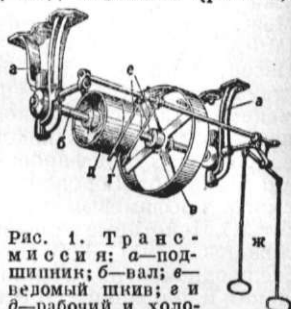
Трансмиссия: а — подшипник; б — вал; в — веревный шкив; г и д — рабочий и холостой шкивы; е и ж — приспособление для перекидывания ремня с одного шкива на другой.
